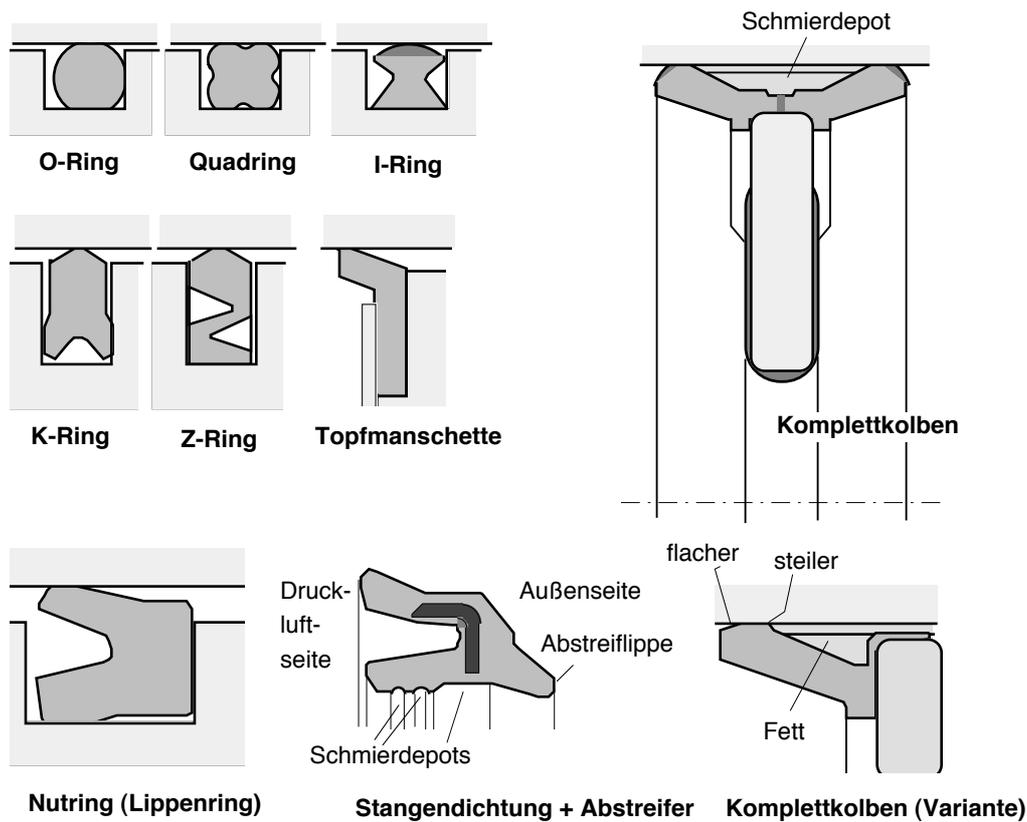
Bauformen von Elastomer - Pneumatikdichtungen
